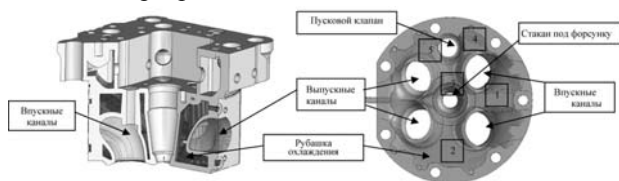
Твердотельная модель крышки цилиндра (а) и схема днища крышки цилиндра (б)
